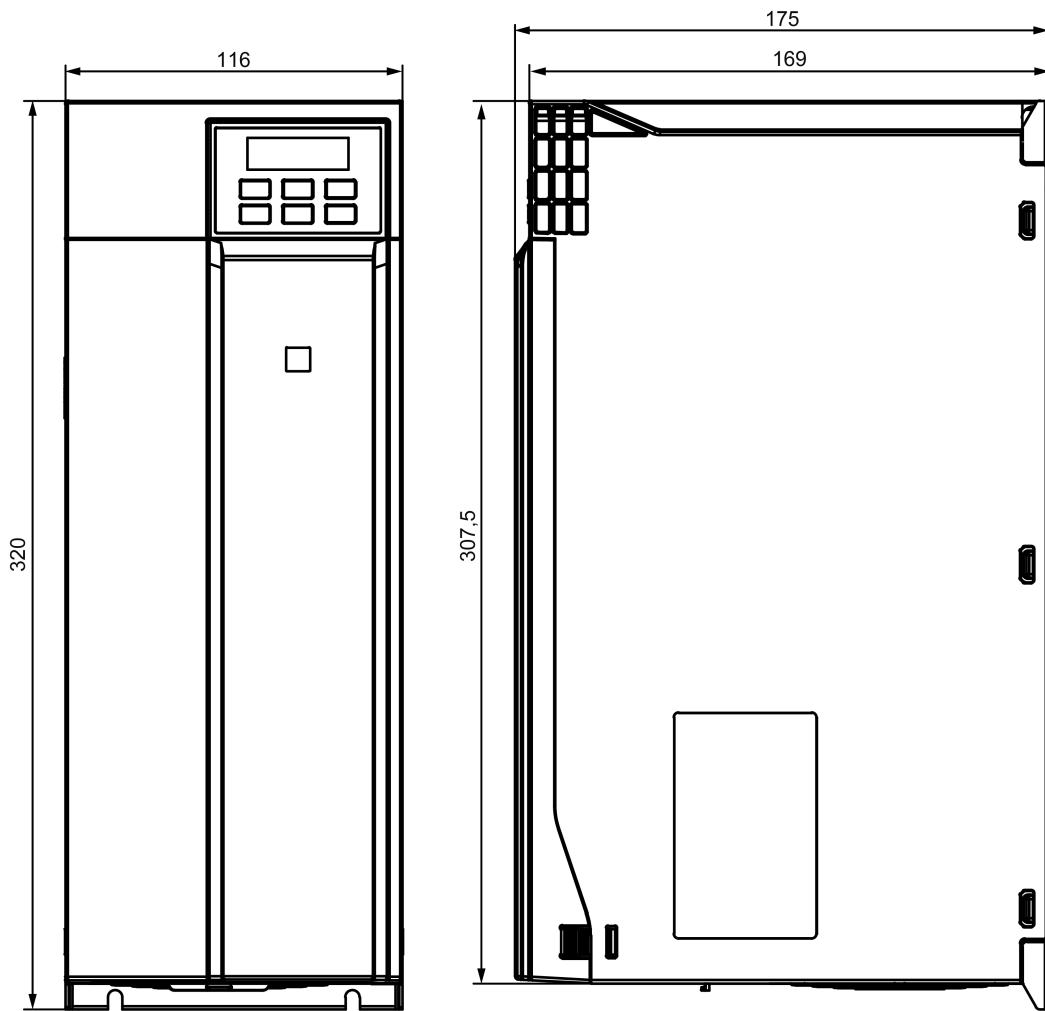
Габаритные размеры прибора в корпусе типоразмера 3
